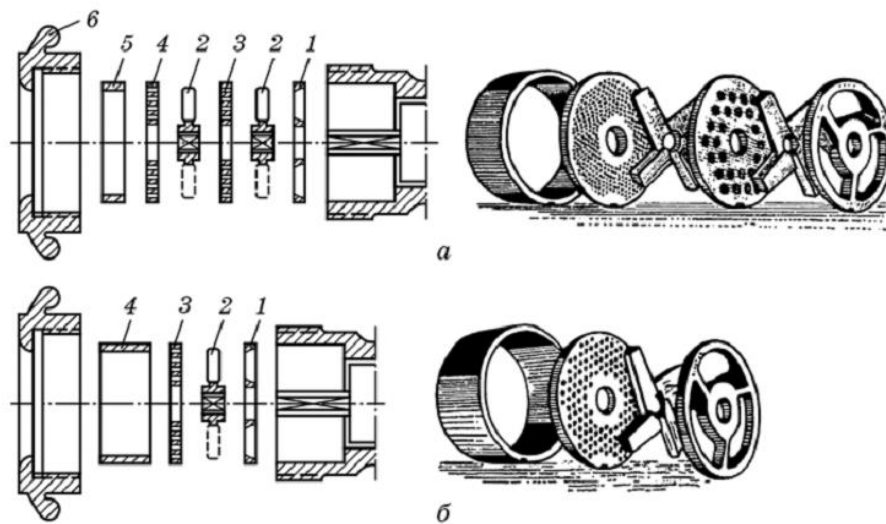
Механізм подрібнювальний: *а* – дрібне подрібнення: 1 – решітка приймальна; 2 – ніж подвійної дії; 3 – пластина середня; 4 – пластина кінцева (отвори 2-3 мм); 5 – кільце розпірне; 6 – затискний пристрій; *б* – крупне подрібнення: 1 – решітка приймальна; 2 – ніж подвійної дії; 3 – пластина середня (отвори 16-25 мм); 4 – кільце розпірне. [10]
